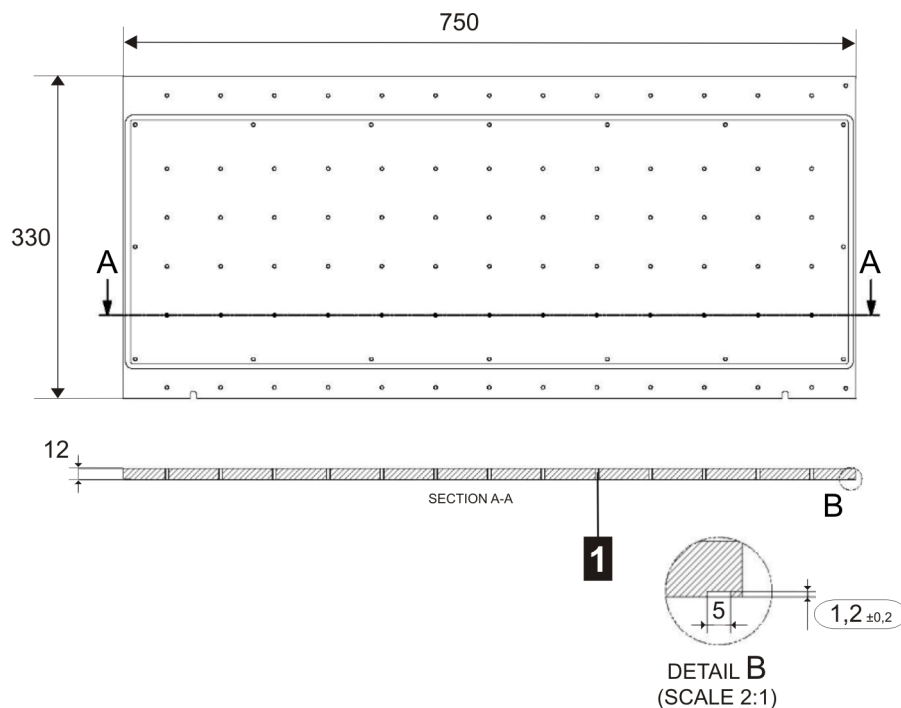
Abmessungen Kühlplatte D3-XM 300-080, Maße in mm
